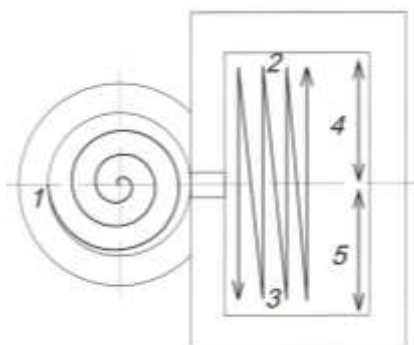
Схема розташування та розгорток променів для плавки зливків сплавів титану
